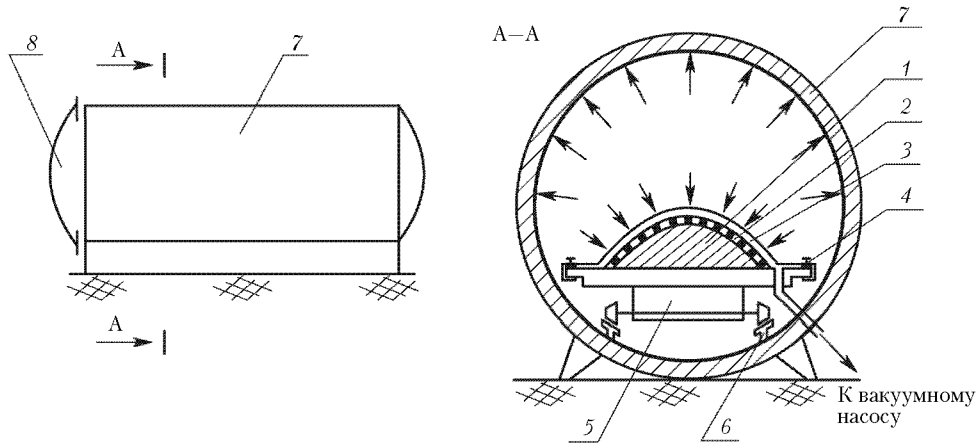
Формование в автоклаве: 1 – форма; 2 – препрег; 3 – эластичная мембрана; 4 – уплотнители; 5 – тележка; 6 – рельсы; 7 – корпус автоклава; 8 – крышка
